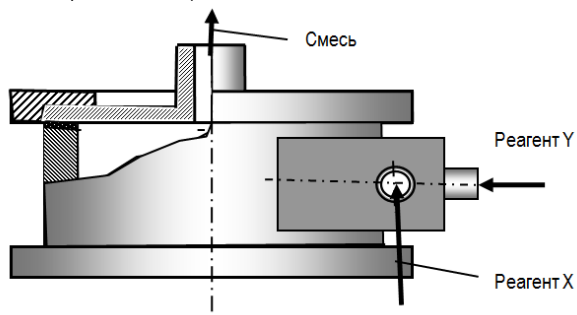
Схема экспериментальной установки вихревого центробежного смесителя
